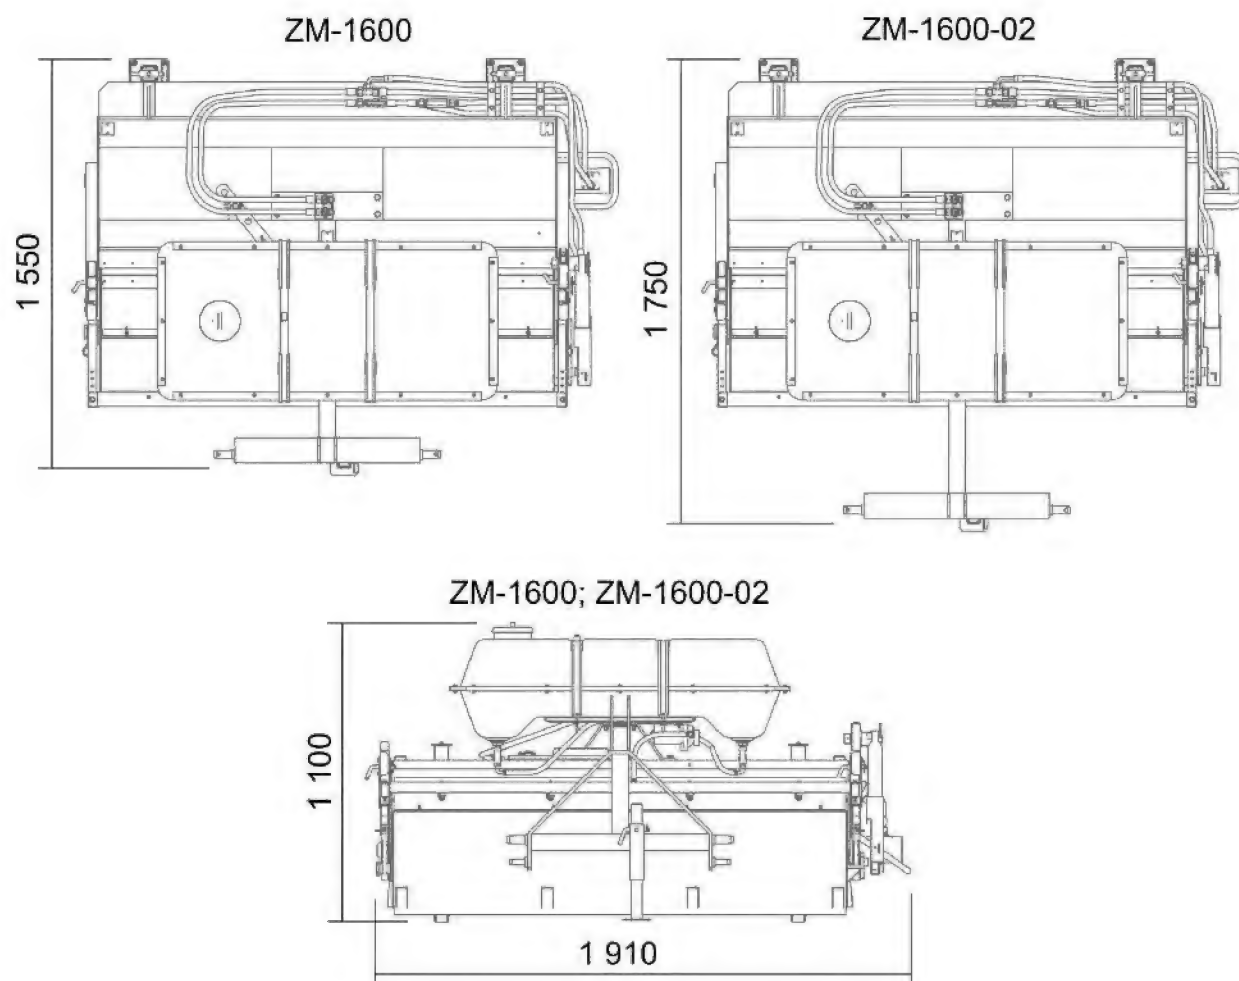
A Dimensions externes ZM-1600; ZM-1600-02
